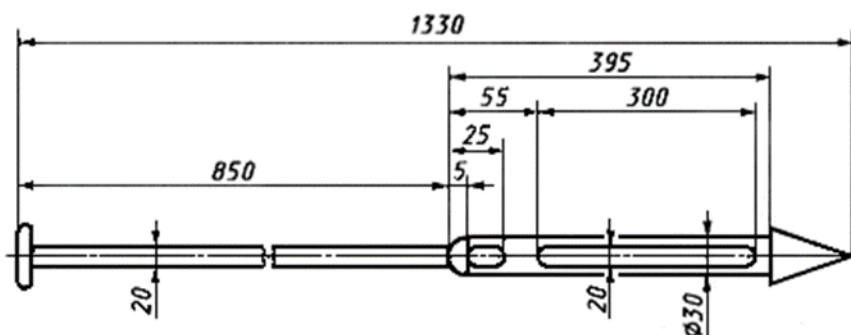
Внешний вид ручного щелевидного пробоотборника.
